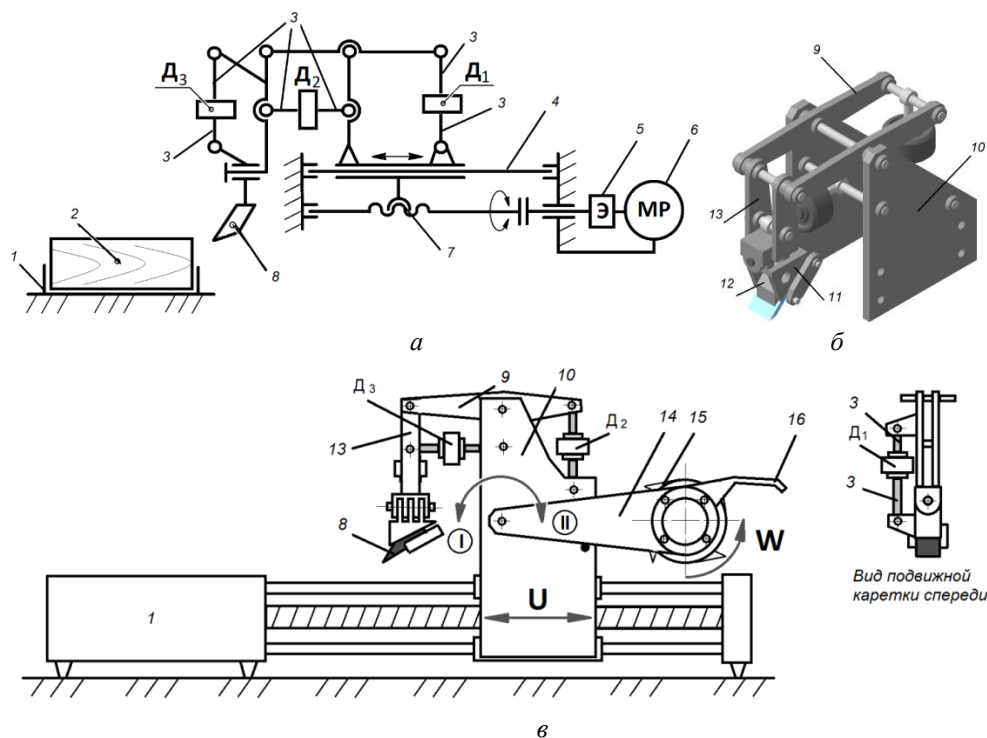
Устройство для дендрохронологических исследований древесины простым резанием: *а* – кинематическая схема устройства; *б* – модель подвижной каретки; *в* – компоновка устройства; 1 – стол для закрепления образца; 2 – исследуемый образец; 3 – датчики (растяжения/сжатия) D_1 , D_2 , D_3 ; 4 – линейные направляющие; 5 – энкодер; 6 – механизм надвигания резца (мотор-редуктор); 7 – винтовая передача; 8 – резец; 9 – стрела; 10 – каретка; 11 – державка; 12 – клинообразная пластина для зажатия и фиксации резца в державке; 13 – рукоятка; 14 – рамка; 15 – прорезные фрезы и привод их вращения; 16 – опоры
